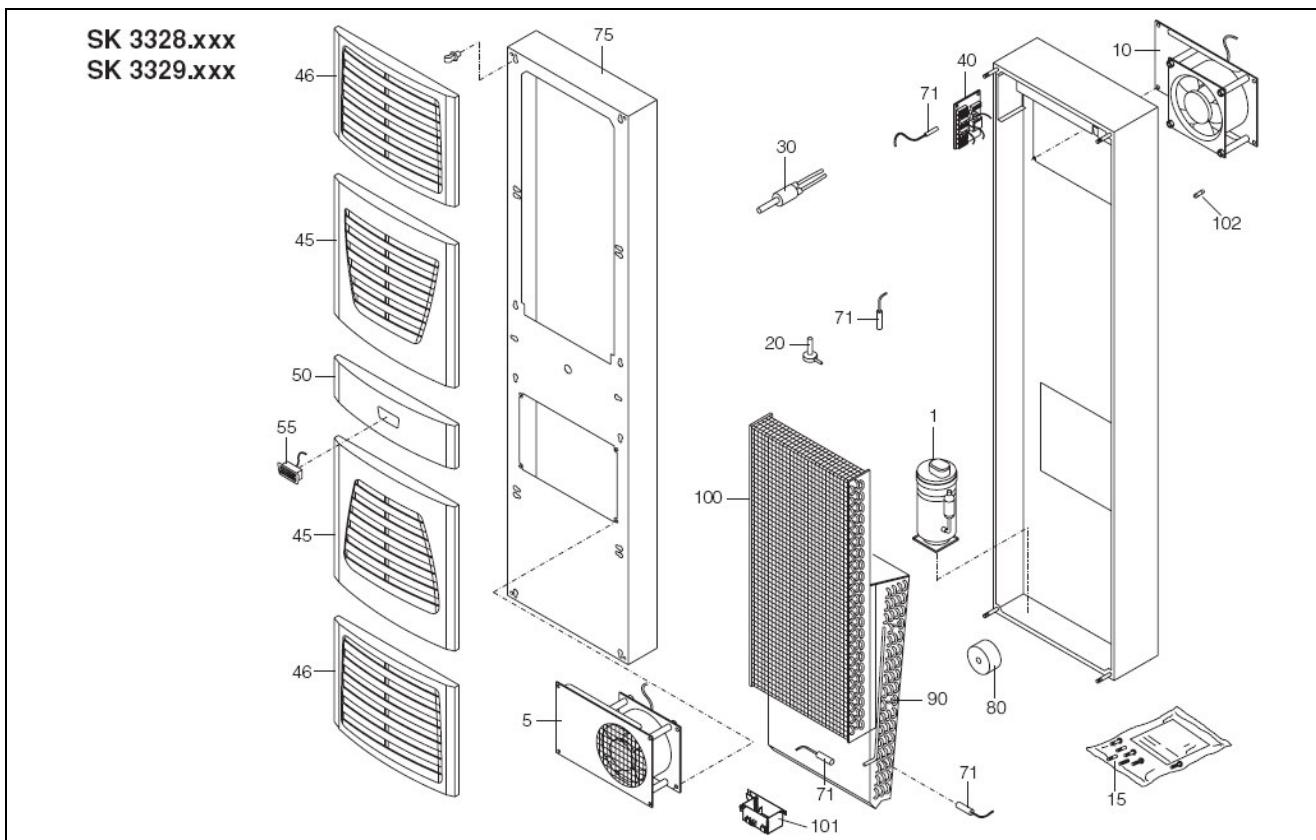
SK 3328.xxx 型和SK 3329.xxx 型的备件
